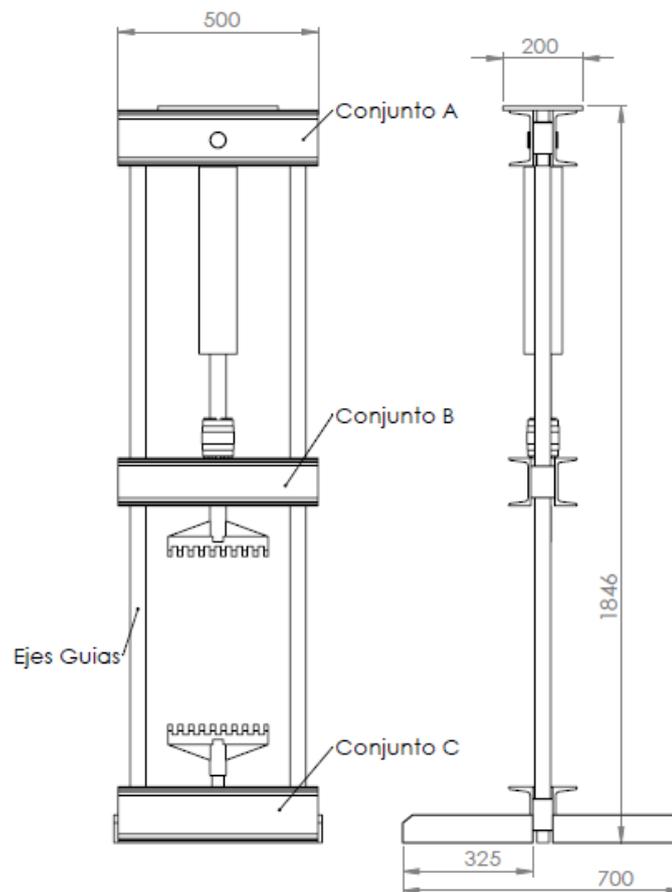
Planos de alzado y planta del banco de ensayos.
